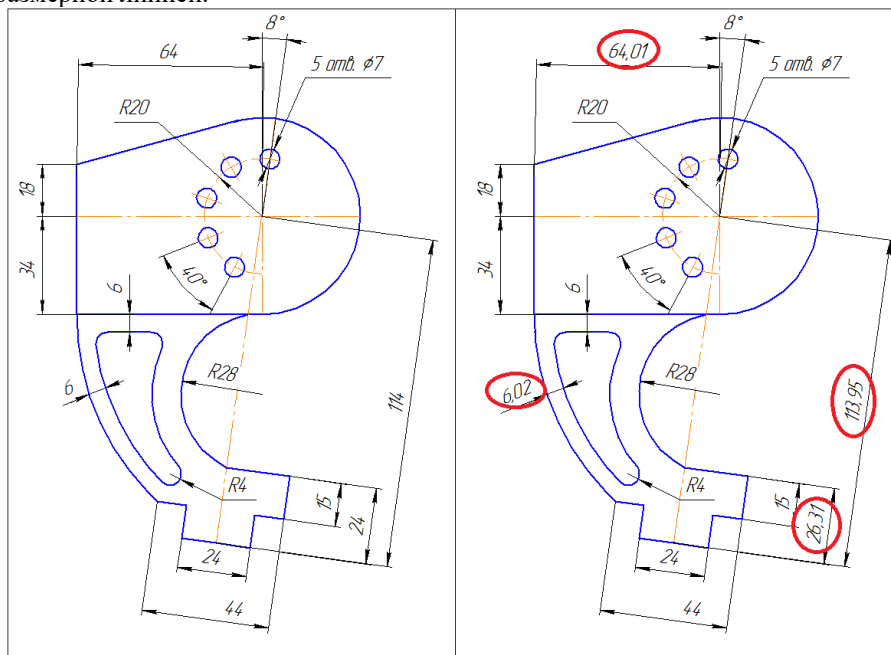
Пример чертежа с различающимися длинами отрезков и размерным числом
